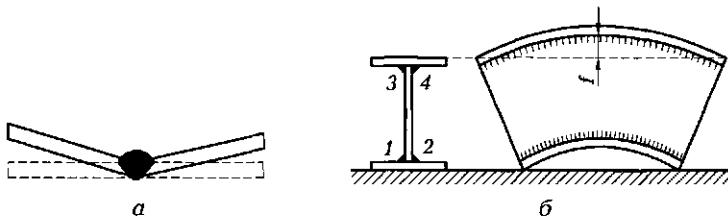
Деформации сварного стыкового соединения (а) и сварной двутавровой балки (б):
